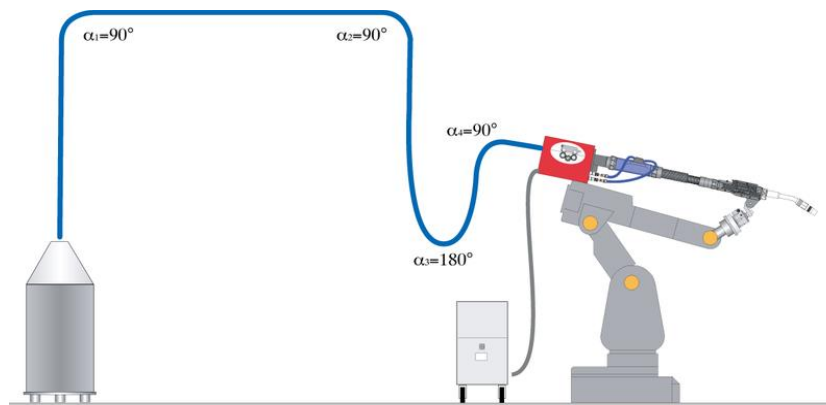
Trajeto do fio de soldadura [76]
